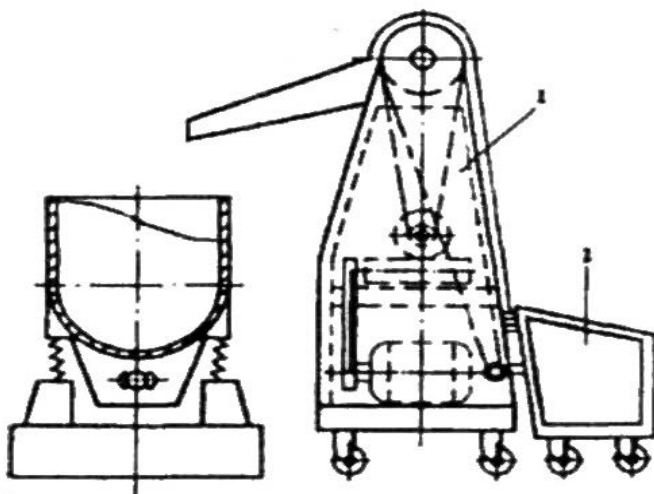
Передвижное механизированное устройство для загрузки обрабатываемых деталей или среды
